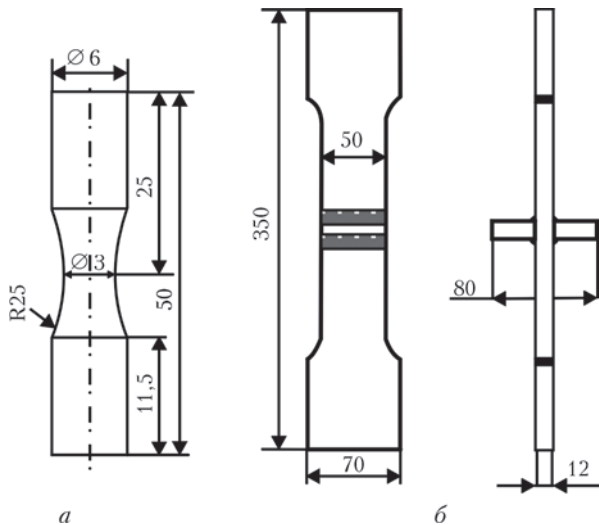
Схематическое изображение образцов для усталостных испытаний; а – круглый галтельный образец; б – образец с тавровыми сварными соединениями для испытаний на усталость в коррозионной среде
